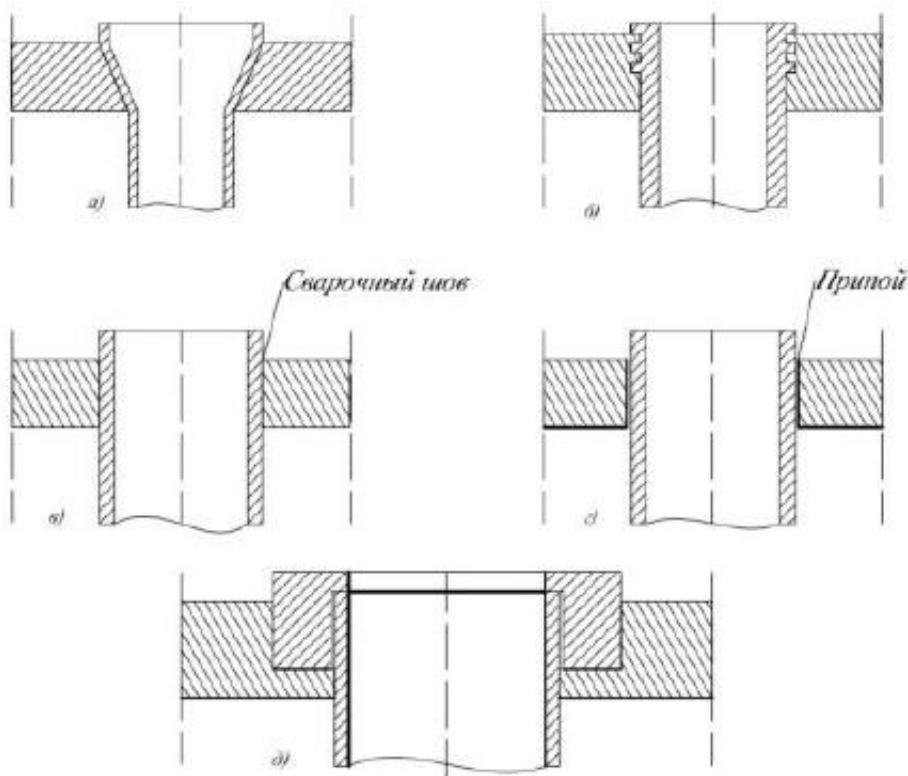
Способы крепления труб в трубных решетках: а – развальцовкой; б – развальцовкой с канавками; в – сваркой; г – пайкой; д – сальниковыми устройствами
